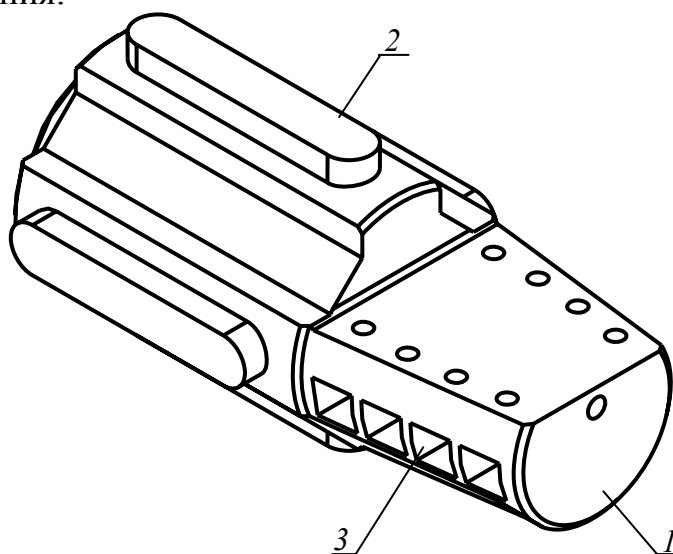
Расточная головка старой конструкции с деревянными направляющими
